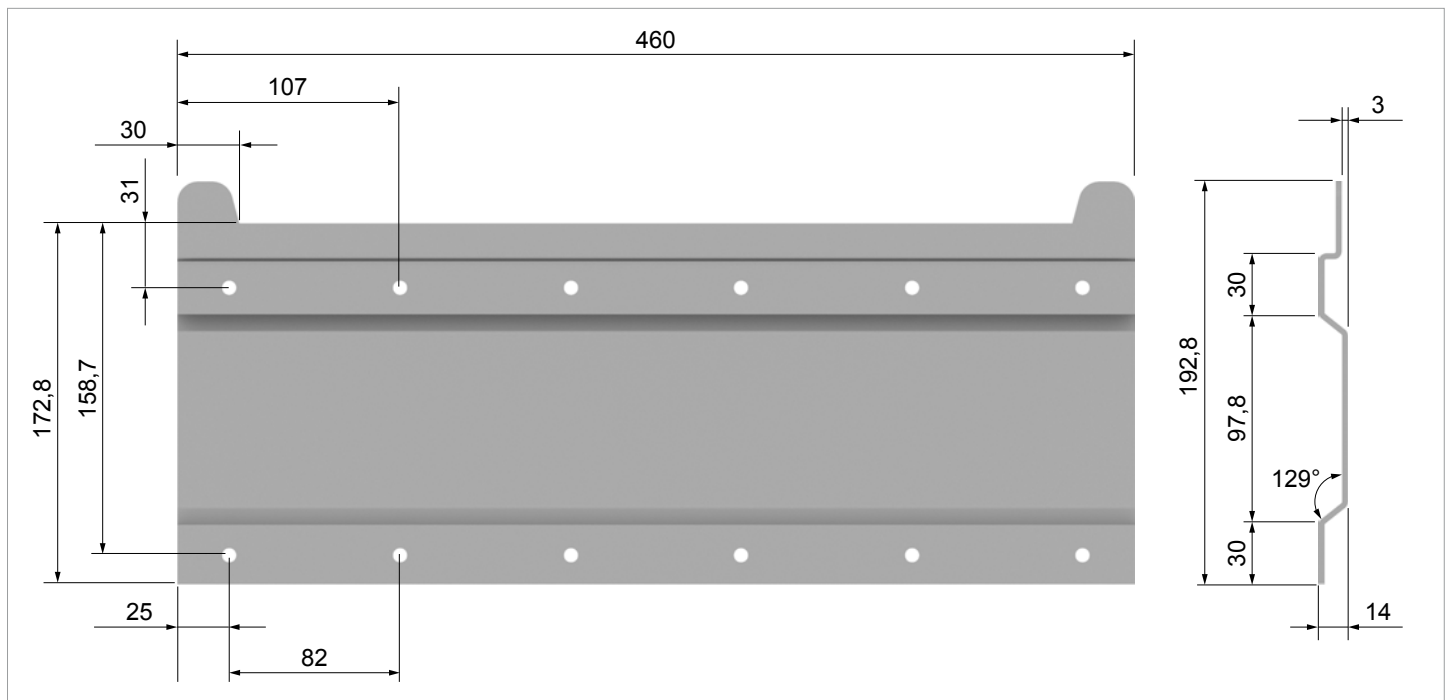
Dimensions de la plaque de montage (en mm)
